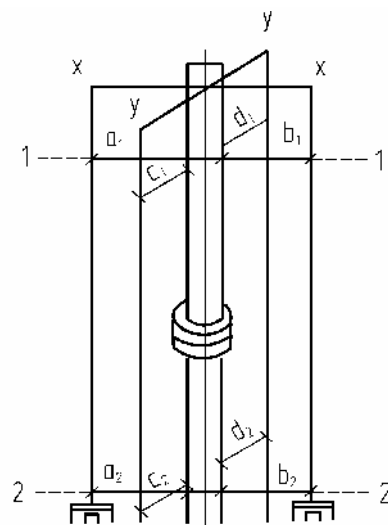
Выверка вертикального вала агрегата с помощью четырех струн
